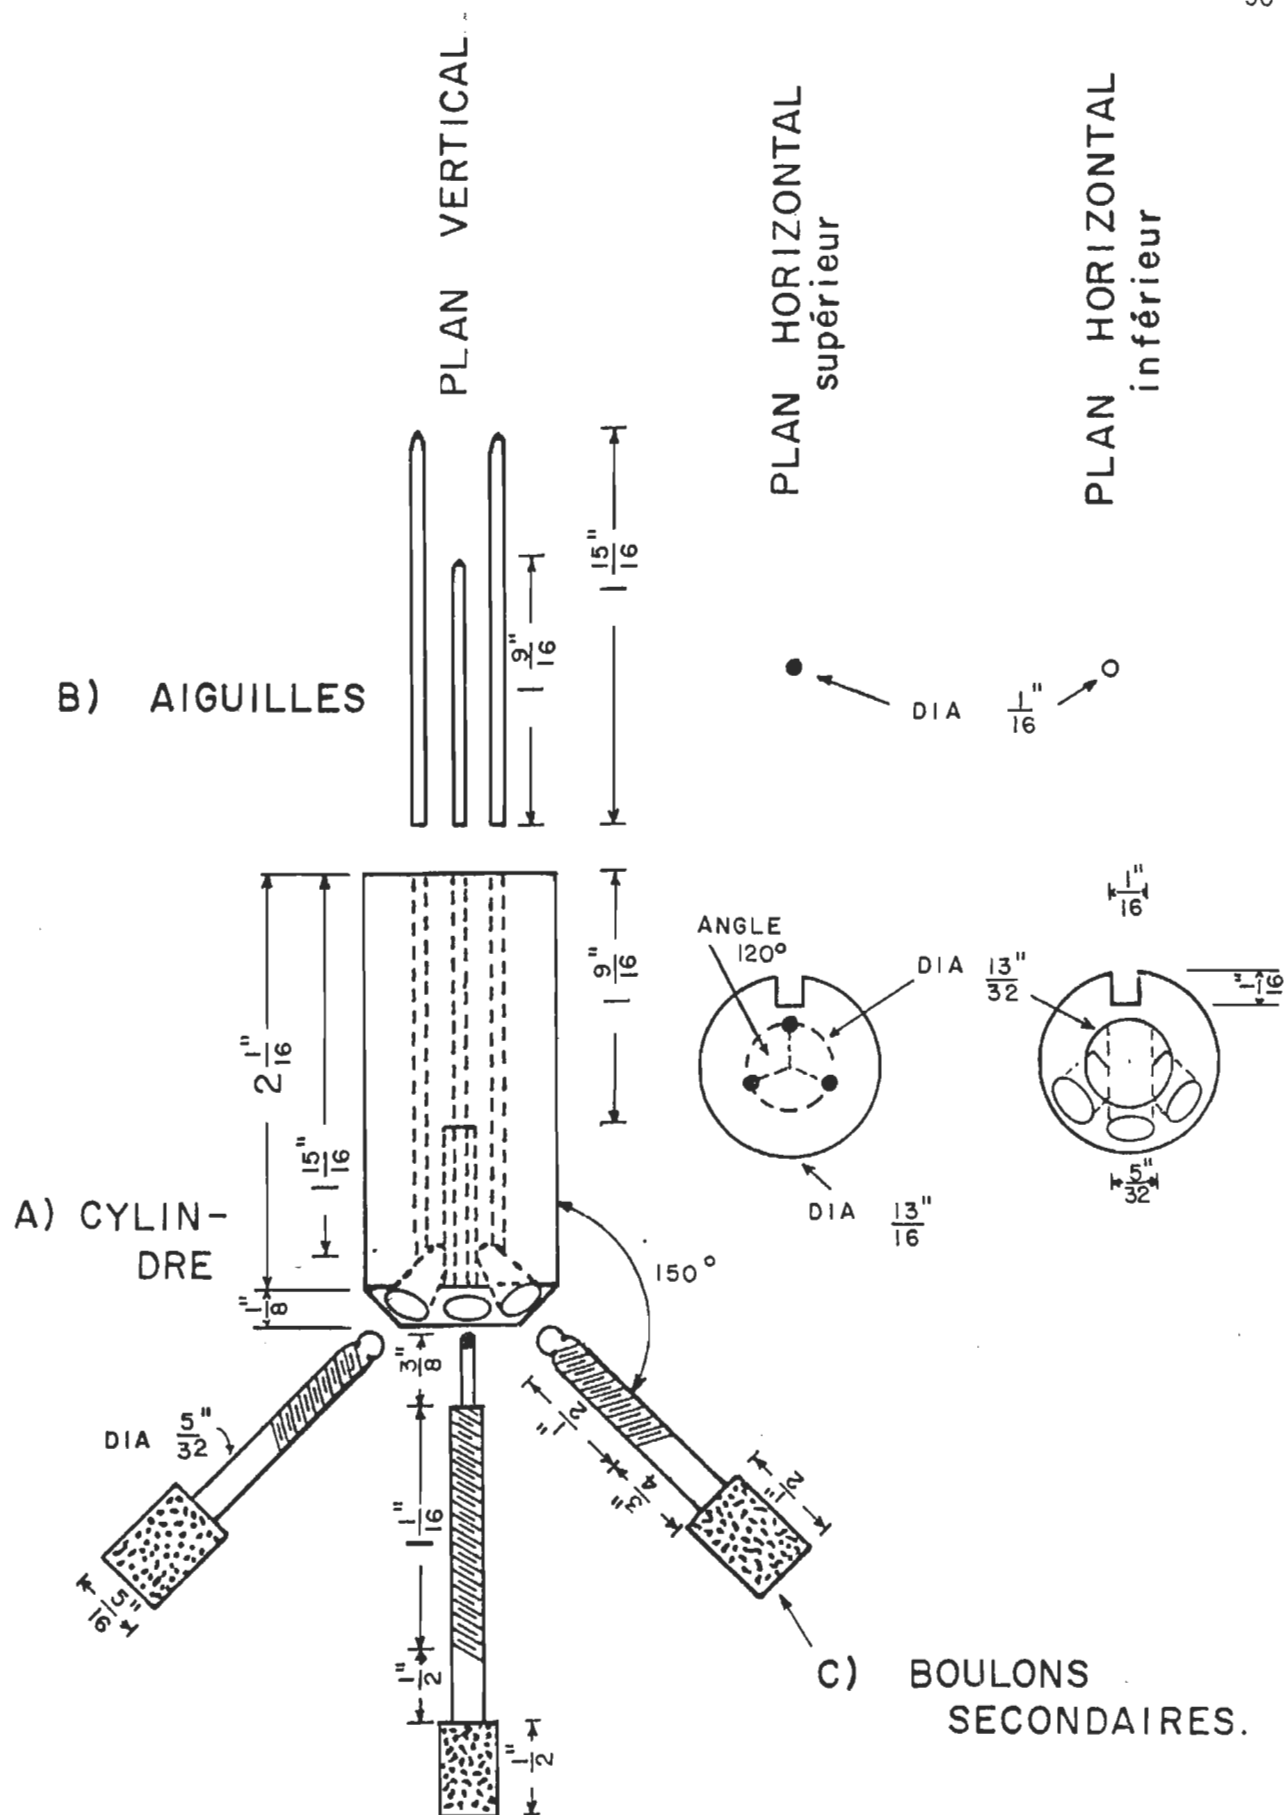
Plan détaillé de la section e comprenant les aiguilles et les boulons secondaires.
